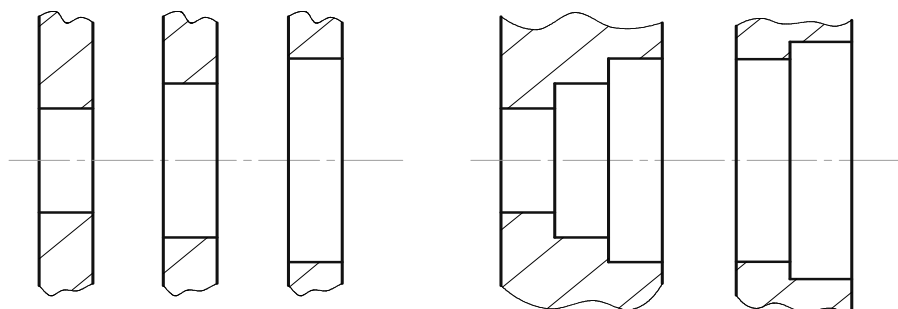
О выборе конструкции основных отверстий корпусной детали
